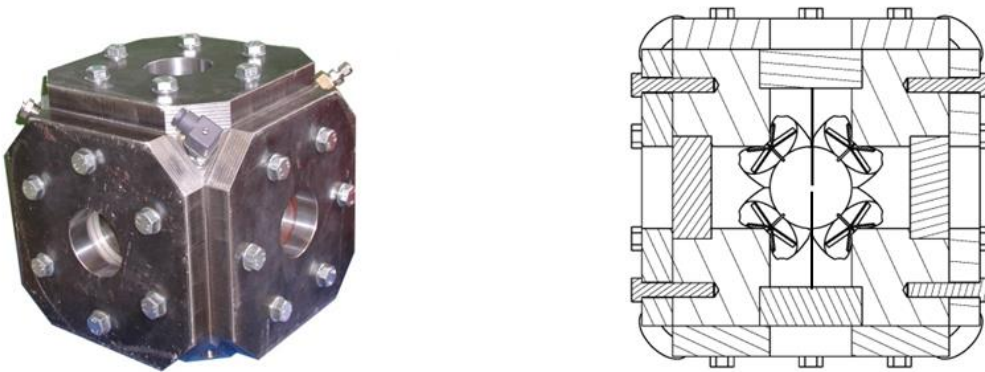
Explosionsbehälter: Außenansicht (links) und Querschnitt (rechts) [Wei08]
